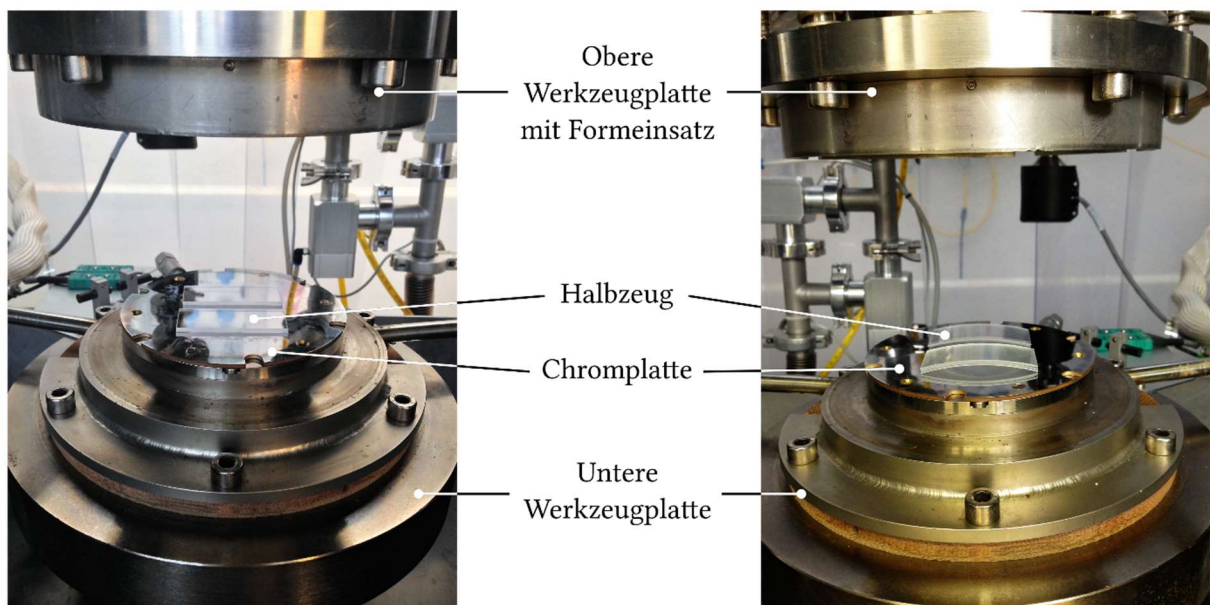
Platzierung der Halbzeuge in Form von PC-Plättchen (links) und PET-Folien (rechts) auf der Chromplatte zum Heißprägen mit dem in der oberen Werkzeugplatte eingebauten Formeinsatz, hier am Beispiel der WUM 02.
